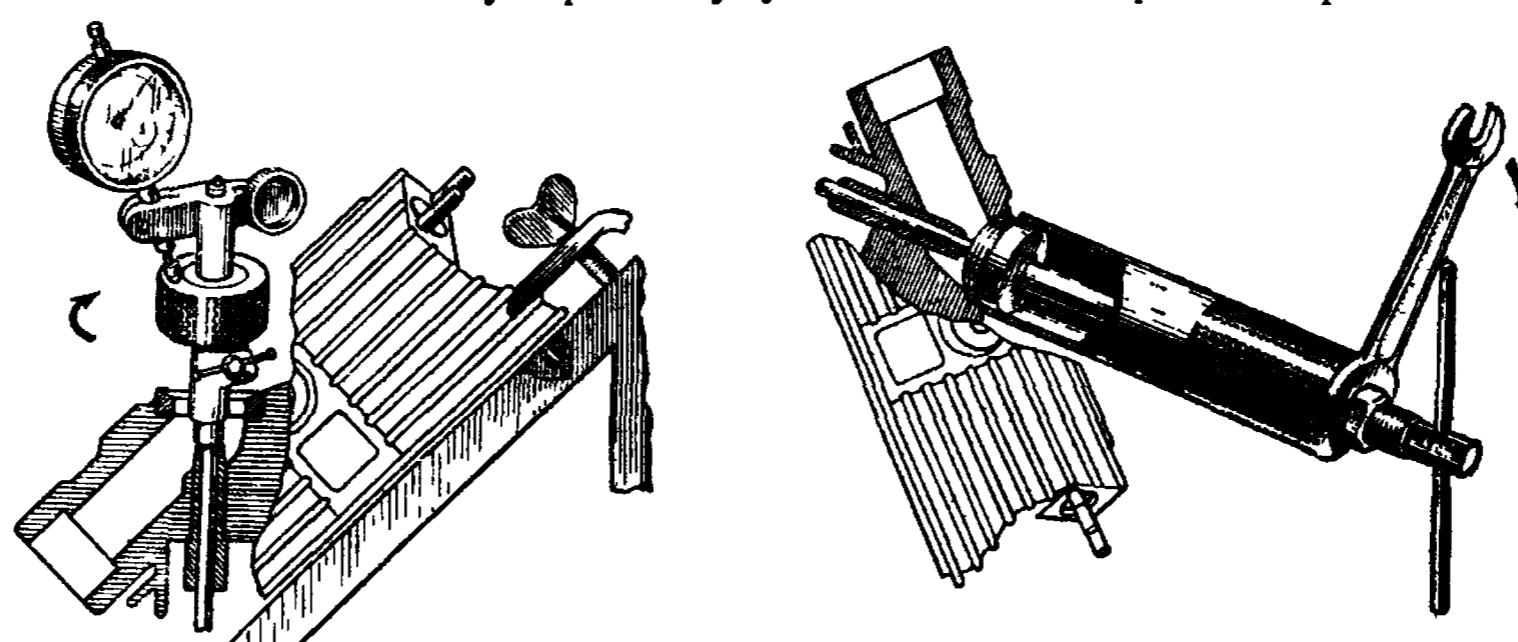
Приспособление для проверки концентричности седла клапана с направляющей втулкой
